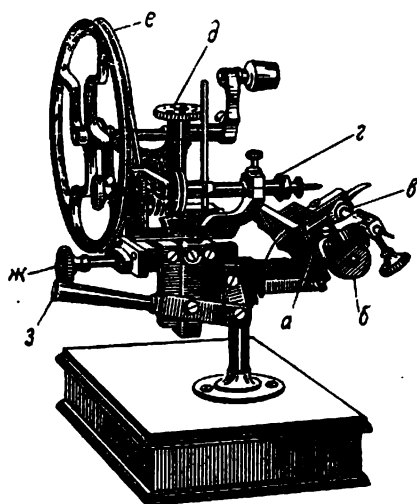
Зубоотделочная машина: *а* — откидной столик; *б* — винт, передвигающий суппорт с фрезеруемой деталью; *в* — деталь между центрами; *г* — фреза; *д* — винт, передвигающий суппорт с фрезой; *е* — маховик; *ж* — регулирующий винт; *з* — рычаг включения
